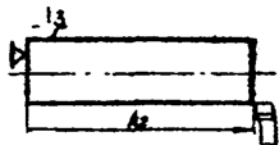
Размерная схема обработки детали "Палец МРЛ"
